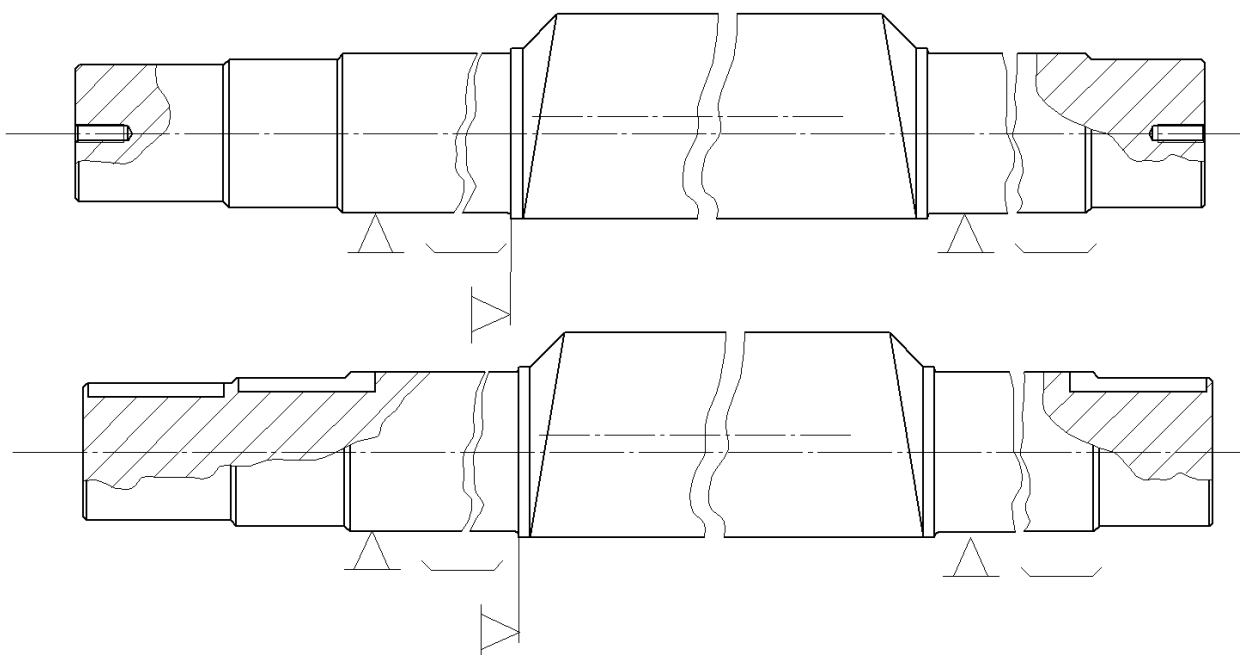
Схема базування на фрезерно-свердлильну обробку
